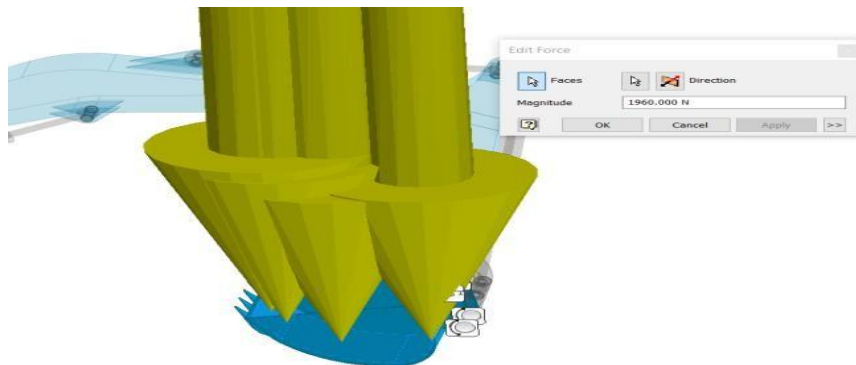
Penentuan posisi fixed constrain pada bucket 3D excavator
